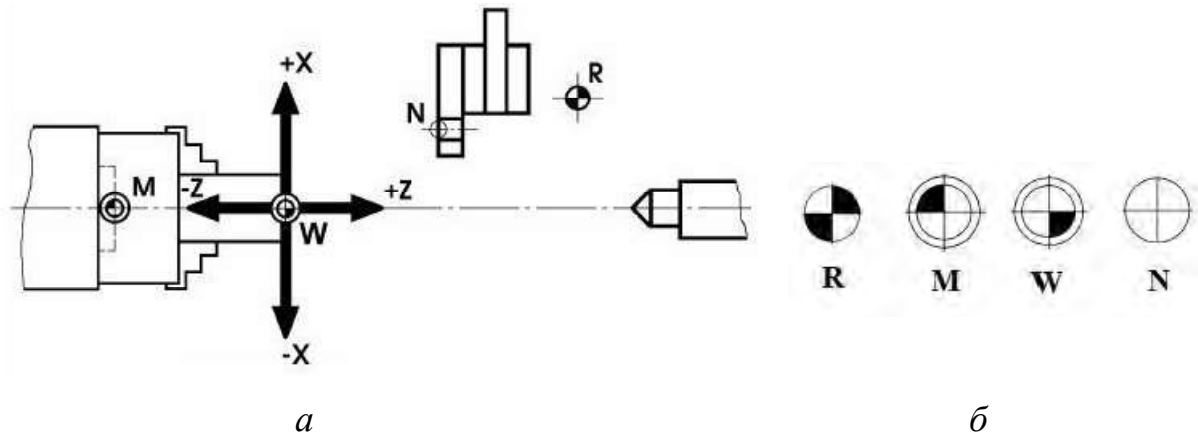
Система координат CNC-верстата та базові опорні точки:
